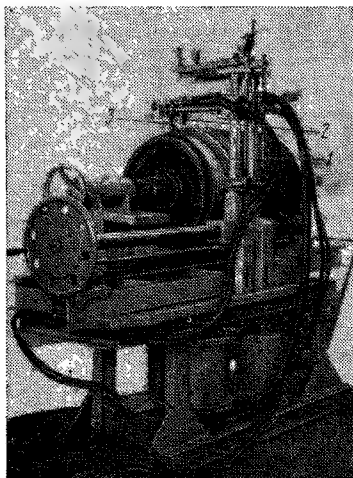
Установка для контактной пайки коллекторов тяговых двигателей:
